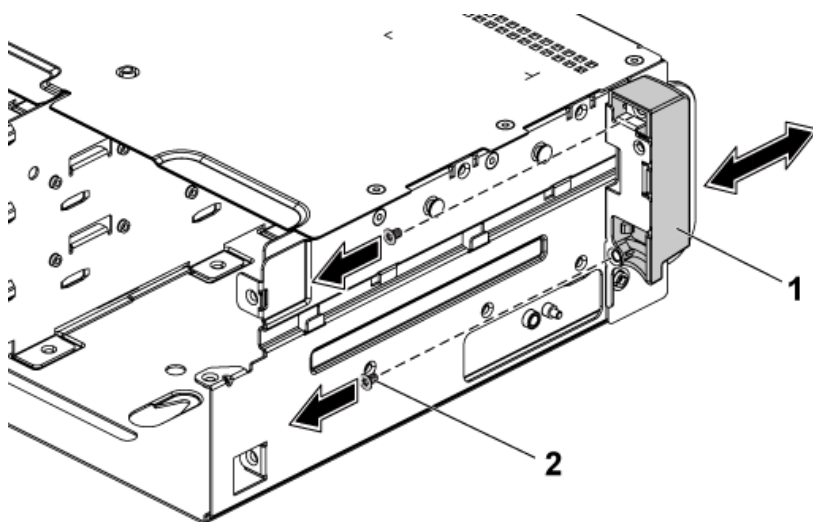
Retrait et installation d'un assemblage de panneau de commande
